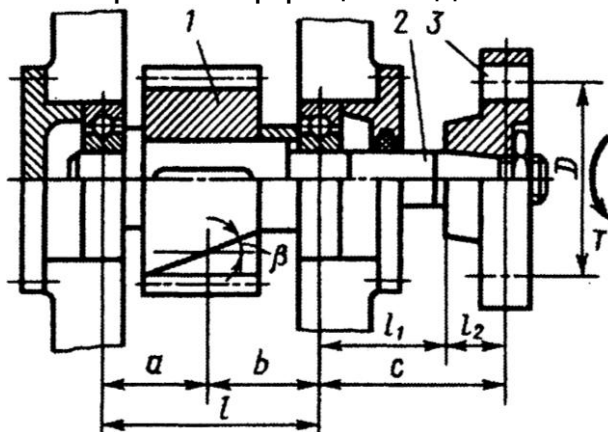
Вал с элементами, расположенными на нем: 1 – шестерня; 2 – вал; 3 – полумуфта
